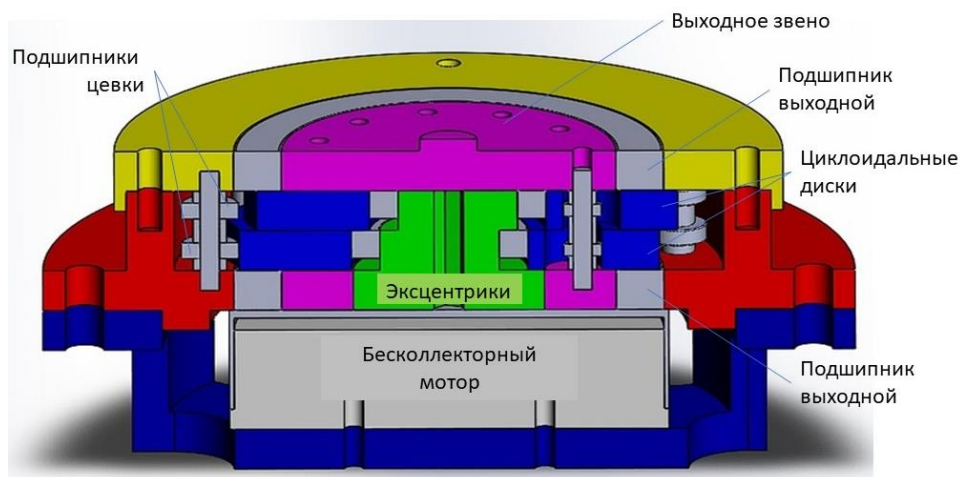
Общий вид и компоновка мотор-редуктора
